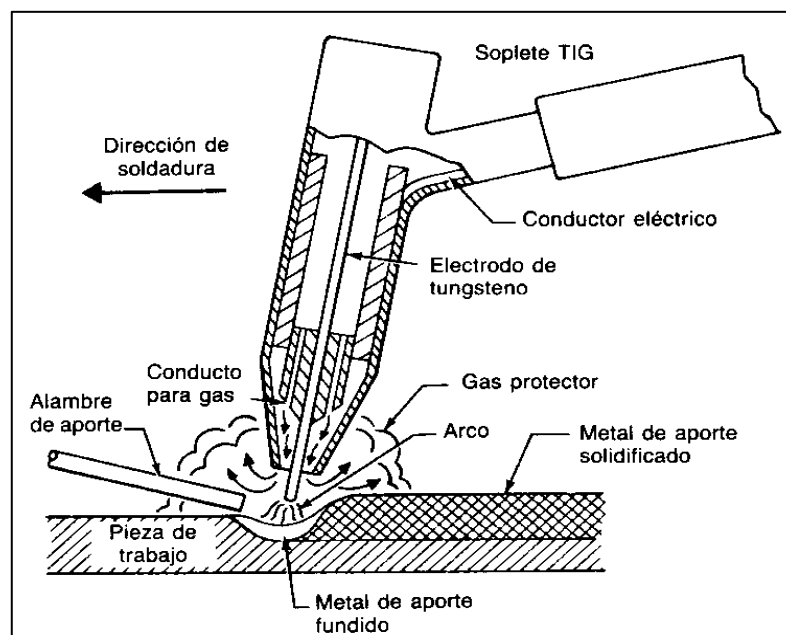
Dibujo de los componentes del porta electrodo para soldadura TIG. Fuente: Slevi1.mit.edu
